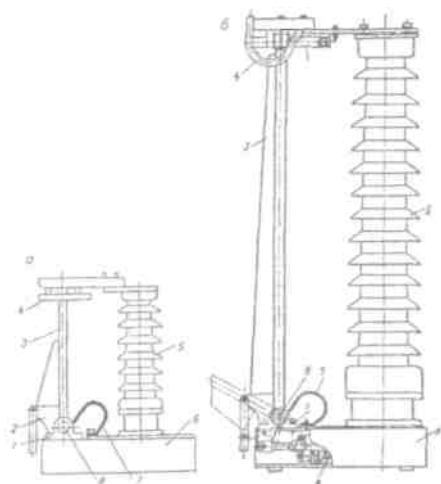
Короткозамыкатели: а - 35 кВ; б - ПО кВ; 1 — подшипник; 2 — тяга привода; 3 — нож короткозамыкателя; 4 — неподвижный контакт; 5 — опорный изолятор; 6 — опорная рама; 7 — гибкая связь; 8 — вал; 9 — привод
